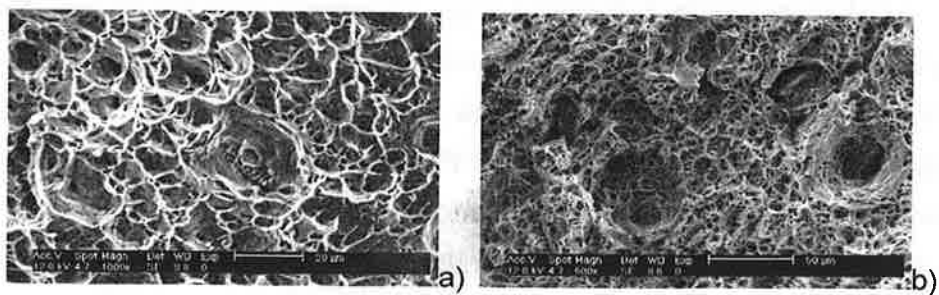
Fractografías de uniones soldadas por fusión ensayadas en la Barra Hopkinson a velocidades de impacto de (a) $v=18$ m/s y (b) $v=25$ m/s.
